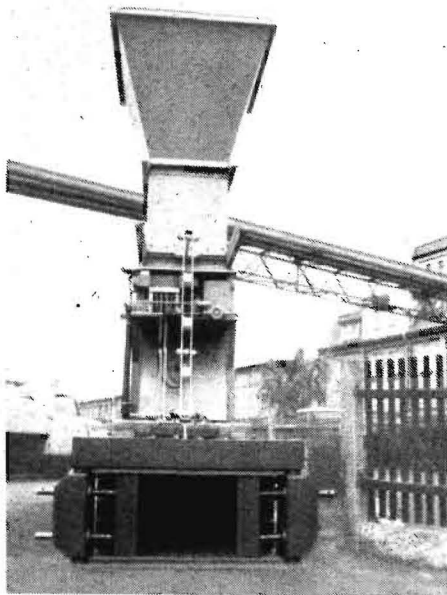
Seitenansicht der Presse; unten durch Gewindespindeln verstellbare Austrittsöffnung des Preßkorbs
